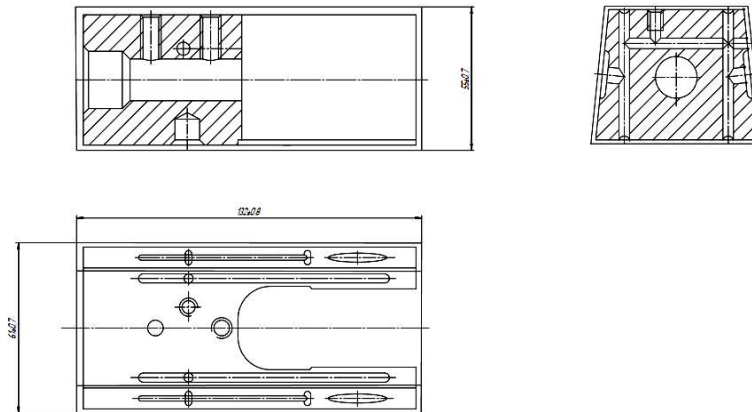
Загальний вигляд зготівки «Повзун»
